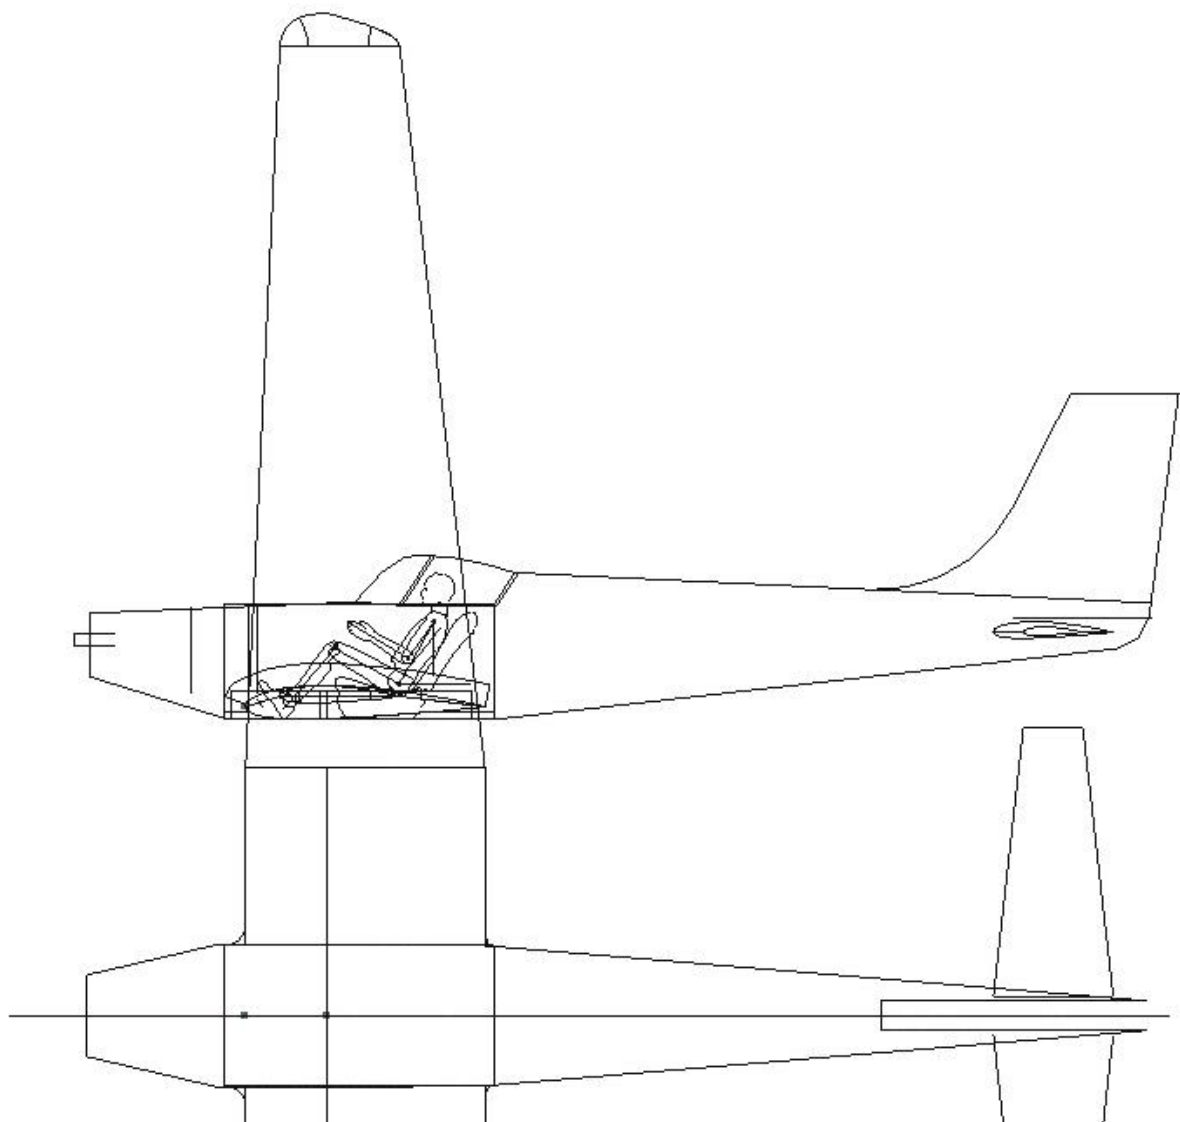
1º Desenho CAD – Bi-Dimensional
